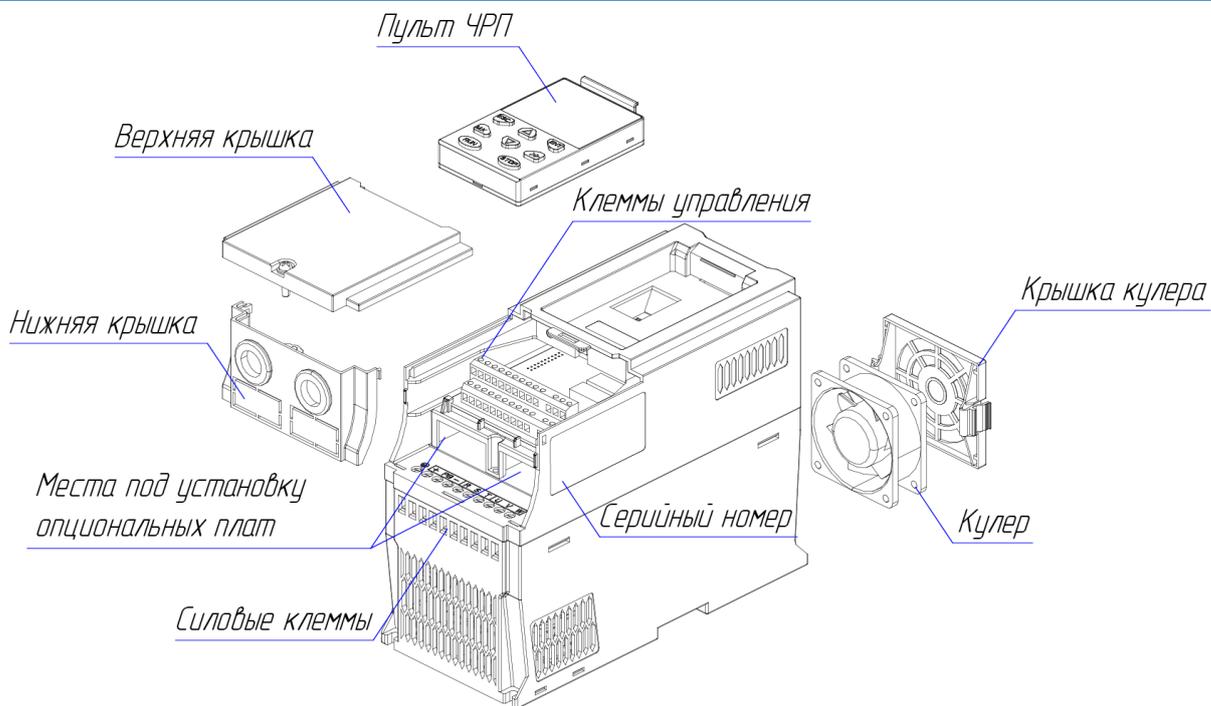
Общий вид VFD500 пластиковый корпус
